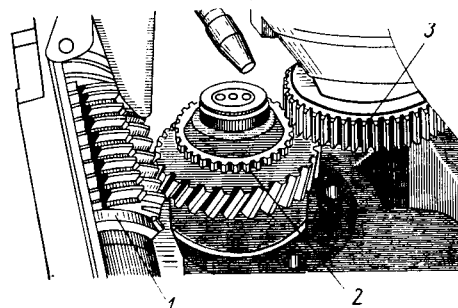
Схема одновременной обработки двухвенцового зубчатого колеса на зубофрезерном станке Комби:
